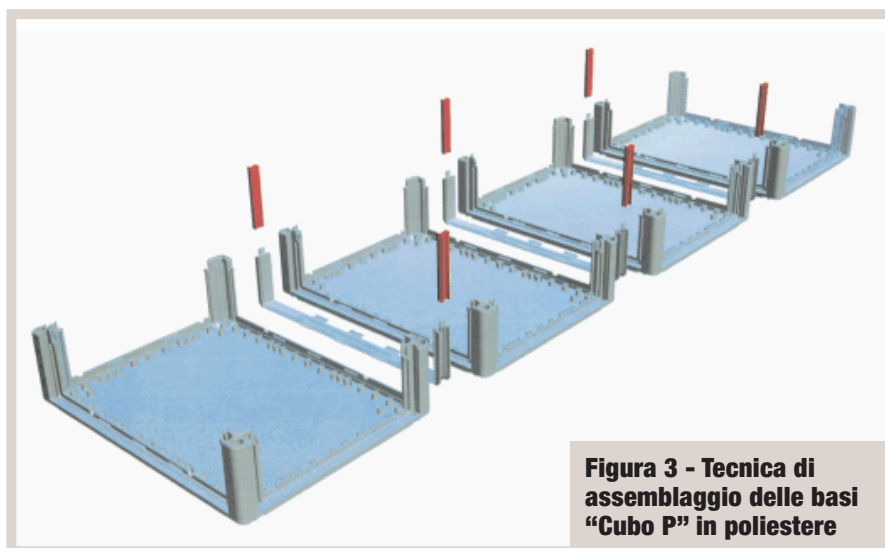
Tecnica di assemblaggio delle basi "Cubo P" in poliuretano
